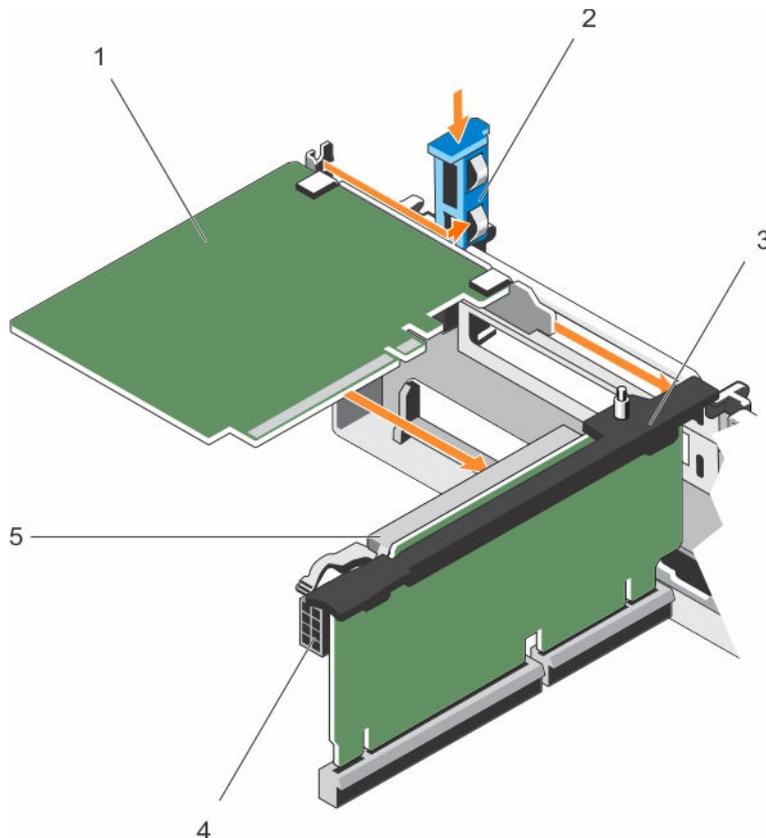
Instalar uma placa de expansão na riser de placa de expansão 2 ou 3
